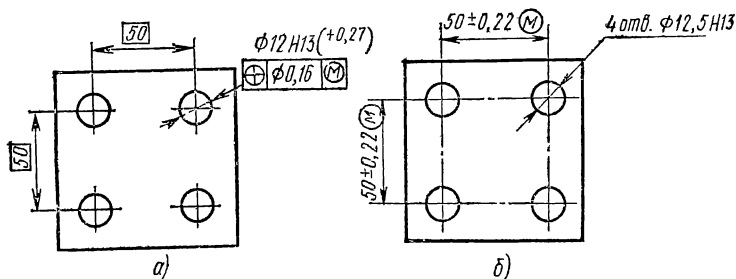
Простановка допусков на расположение осей отверстий:
